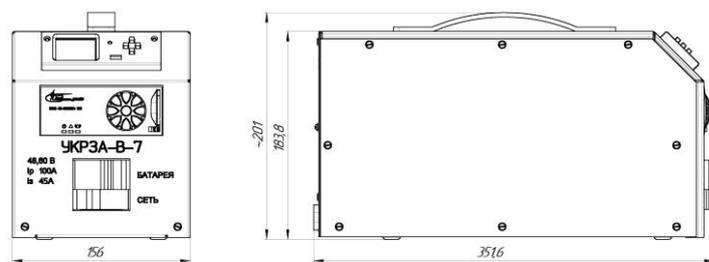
Габаритный чертеж УКРЗА-В-7
